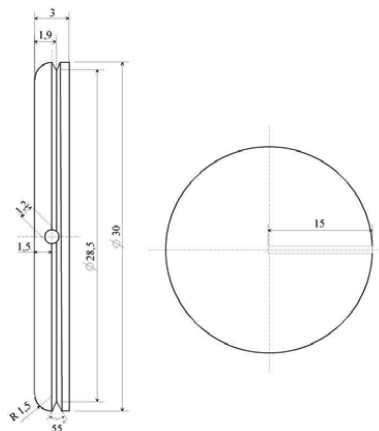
Zeichnung der Geometrie der verwendeten Thermozyklrierproben-Substrate (alle Bemaßungen in mm)
